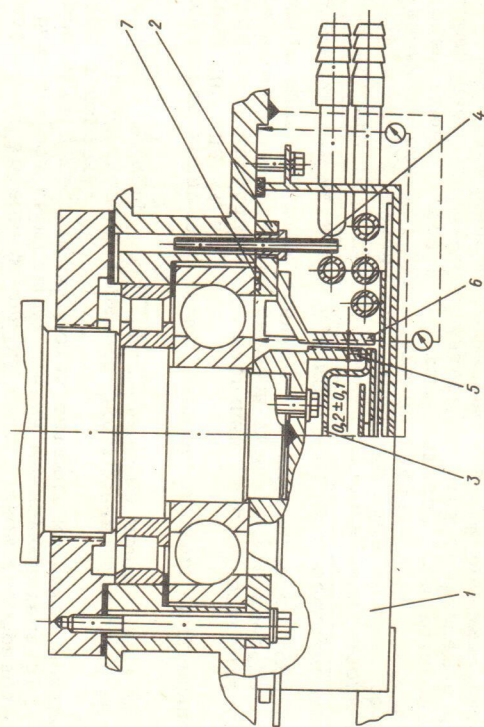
Нижний подшипниковый узел преобразователей типа ППЧВ 250-10,0, ППЧВ 500:
